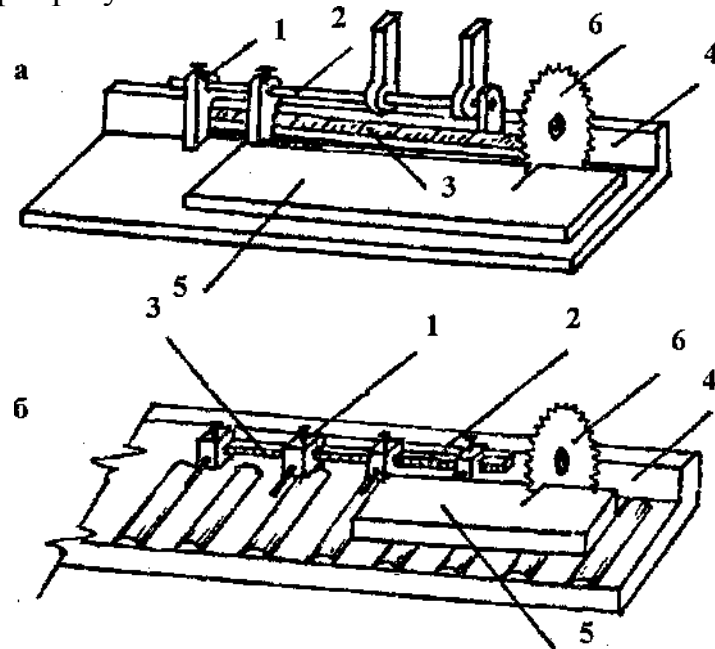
Застосування упорів: а – відкидних; б – утоплюваних; 1 – упор; 2 – штанга; 3 – шкала; лінійка 4 – напрямна; 5 – заготовка; 6 – пила.
